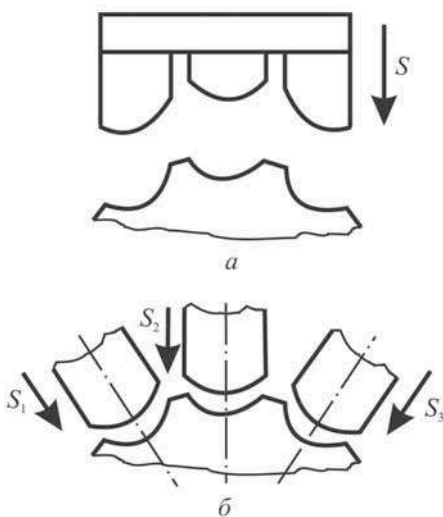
Схемы многорезцовой обработки многозубых деталей
